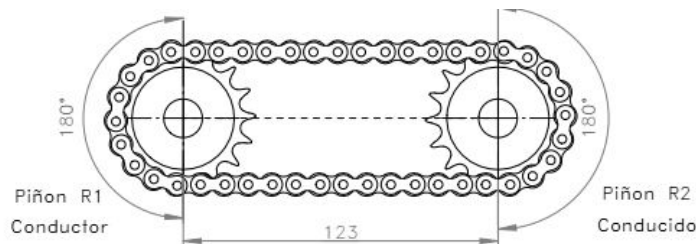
Cadena NO. 35 paso 3/8", transmisión rodillo-rodillo
